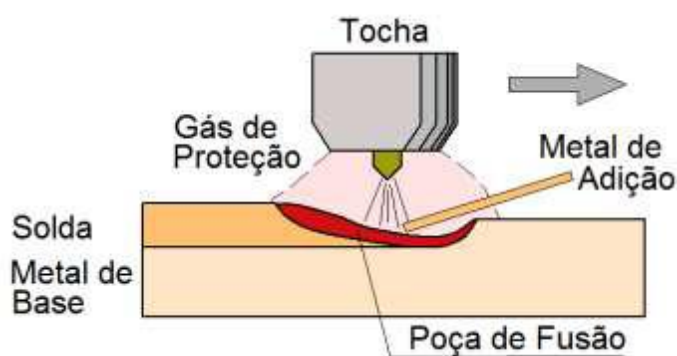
Soldagem GTAW (MODENESI, 2012).
